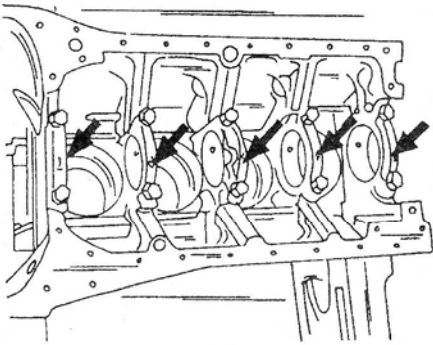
Стрелки указывают на цифровую маркировку крышек подшипников (четырёхцилиндровый двигатель).
